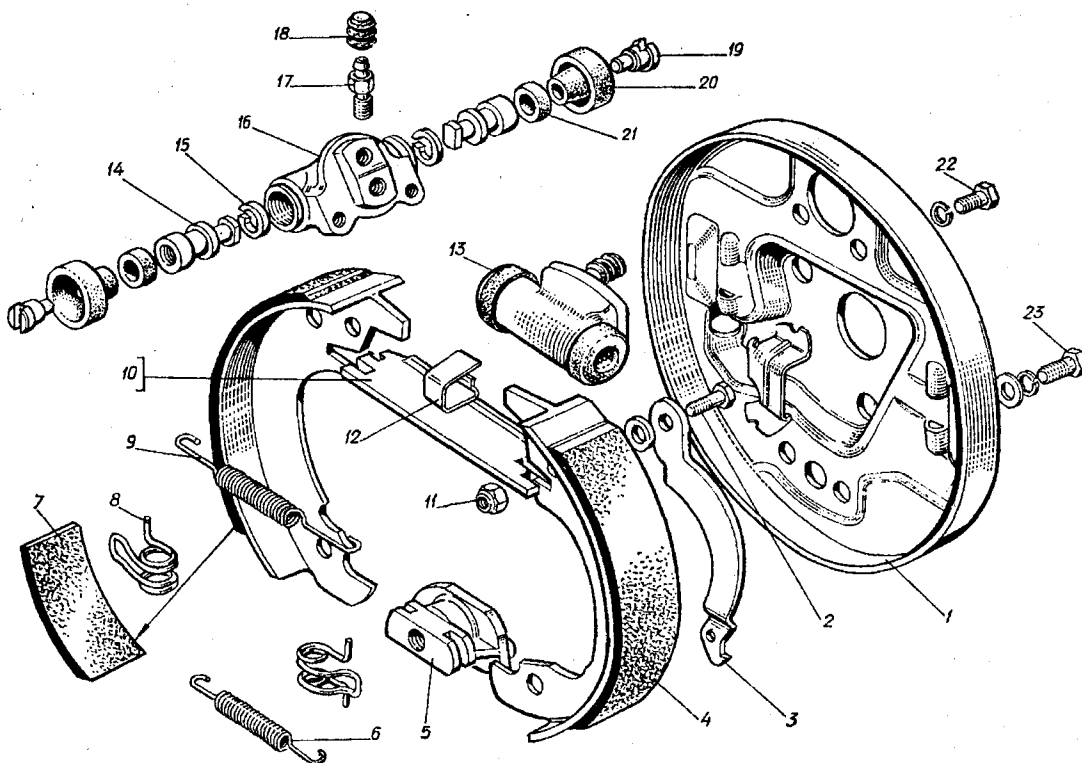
Детали заднего левого тормоза: 1 – шит тормоза; 2 – болт крепления рычага разжимного; 3 – рычаг; 4 – колодка тормоза; 5 – опора колодок; 6 – пружина нижняя; 7 – накладка фрикционная; 8 – пружина прижимная колодок; 9 – пружина верхняя; 10 – планка распорная; 11 – гайка; 12 – пластина демпферная; 13 – цилиндр в сборе; 14 – поршень; 15 – кольцо упорное; 16 – цилиндр; 17 – клапан выпуска воздуха; 18 – колпачок защитный; 19 – стержень; 20 – манжета; 21 – манжета; 22 – болт крепления цилиндра; 23 – болт крепления опоры колодок
